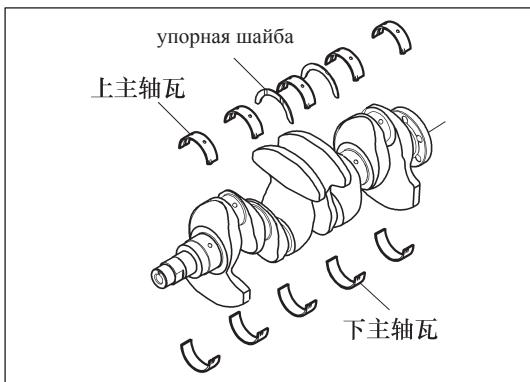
Выбор вкладышей коренных подшипников
